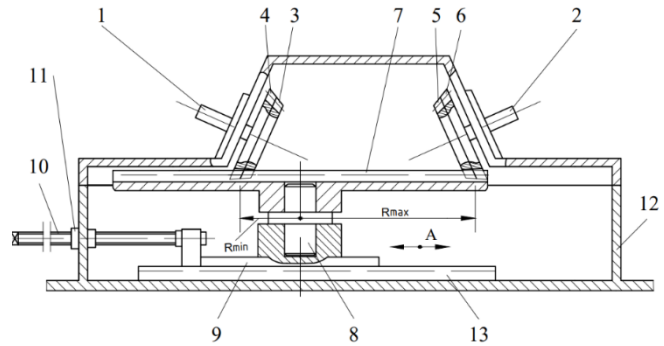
Двухступенчатый вариатор с коническими зубчатыми колесами
